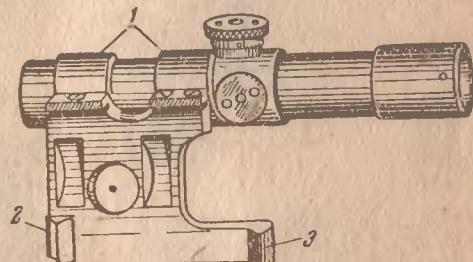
Корпус кронштейна обр. 1942 г.: 1 — хомуты; 2 — шаровая выточка; 3 — выступ
